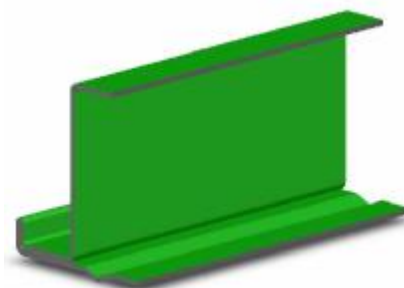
Профиль, изготовленный по схеме рис. 4.6
